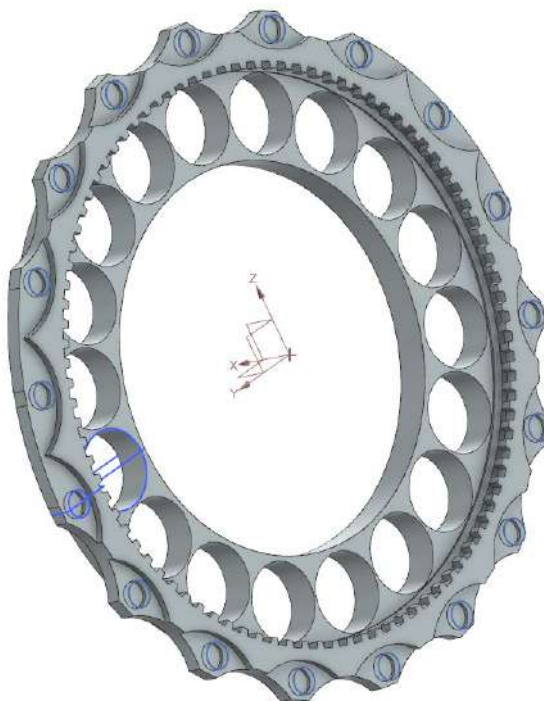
Зображення деталі – циліндр автофлюгування
